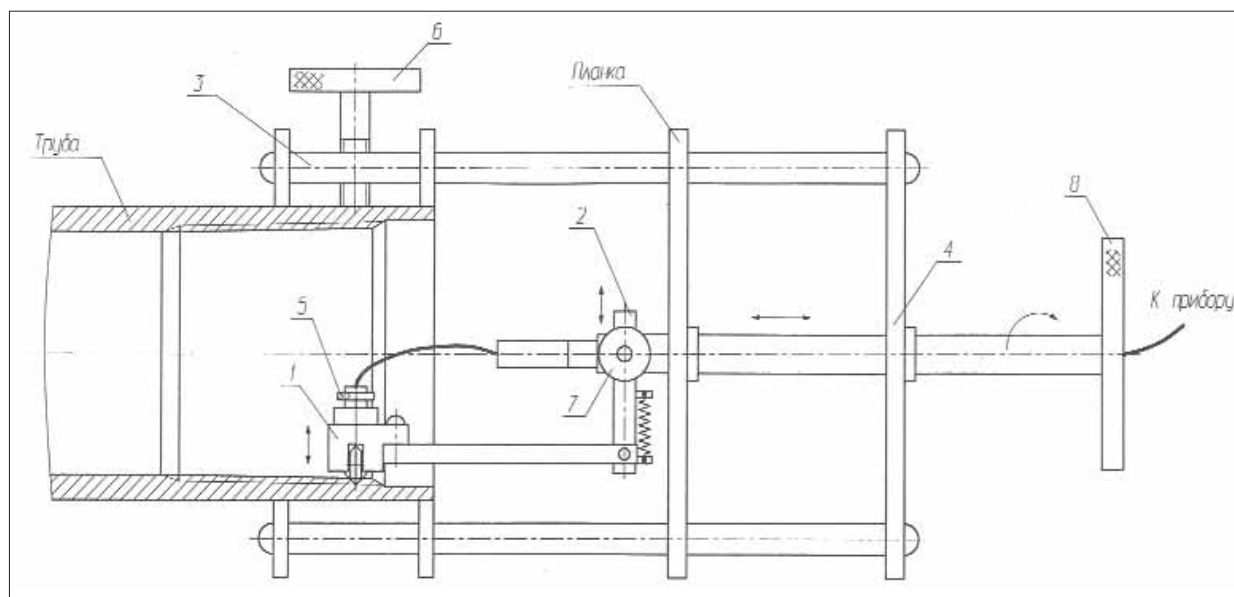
Устройство для механизированного контроля внутренней конической резьбы буровых труб:
